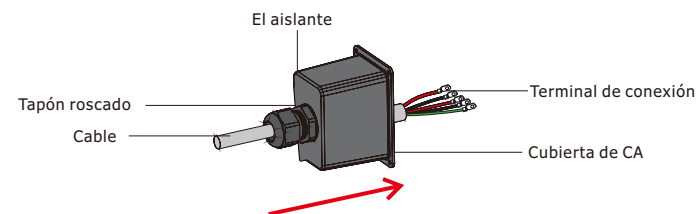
El cable de CA pasa a través de la cubierta del terminal.
